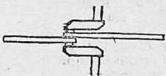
Проверка коленчатого вала на прессе с помощью универсального индикатора в прессе правки
